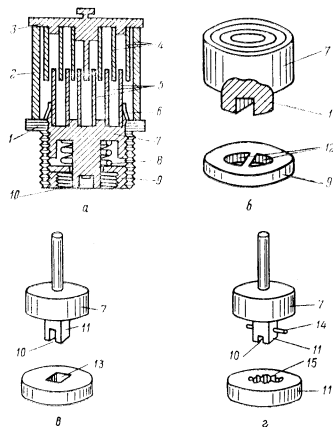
Общий вид (а) и детали механизма регулирования тормозящего момента (б, в, г) воздушного цилиндрического подстроичного конденсатора
